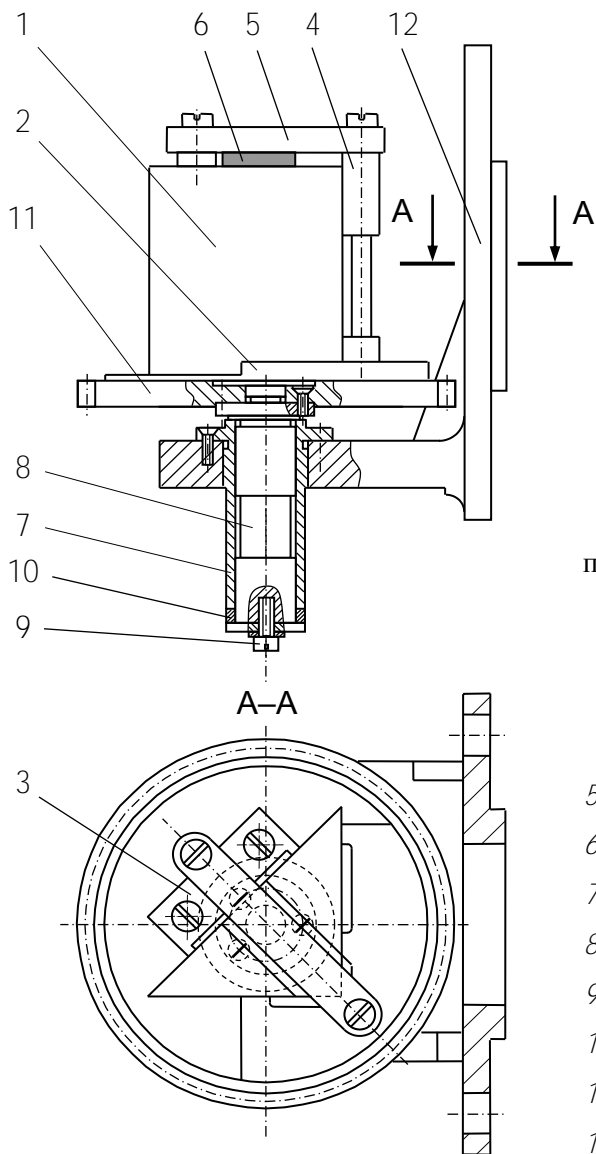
Крепление прямоугольной призмы накладкой:
